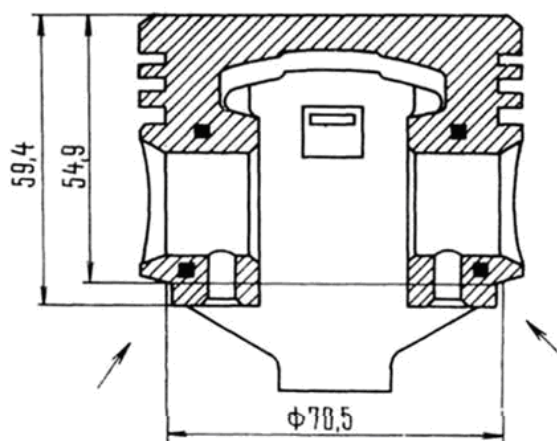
Схема удаления металла с поршня для подгонки его веса.
